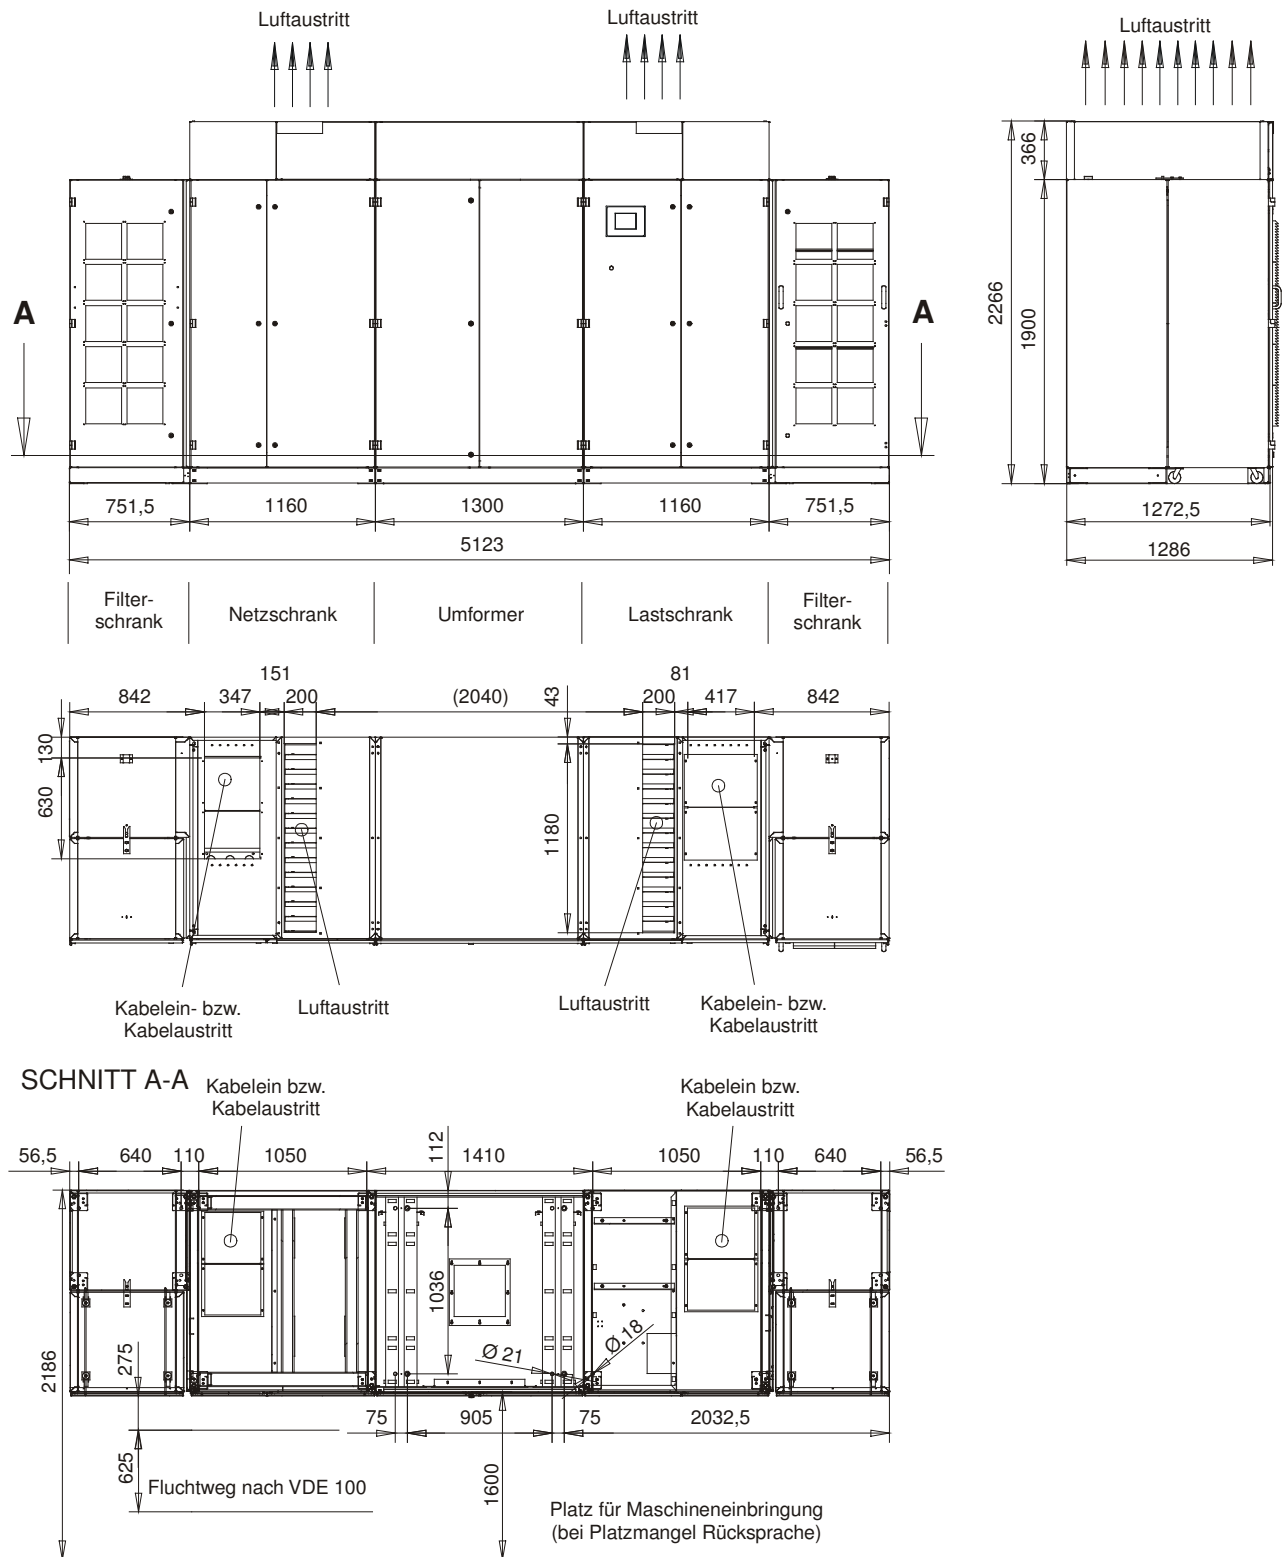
Abmessungen UB800 – UB1100 mit Filterschrank
